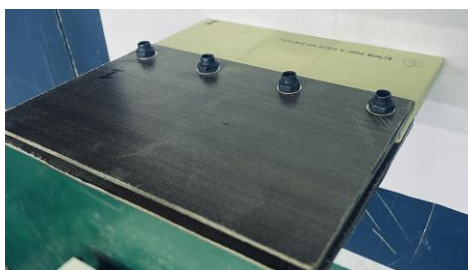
Общий вид конструктивно-подобного образца гибкого элемента в сборке с пластиной
